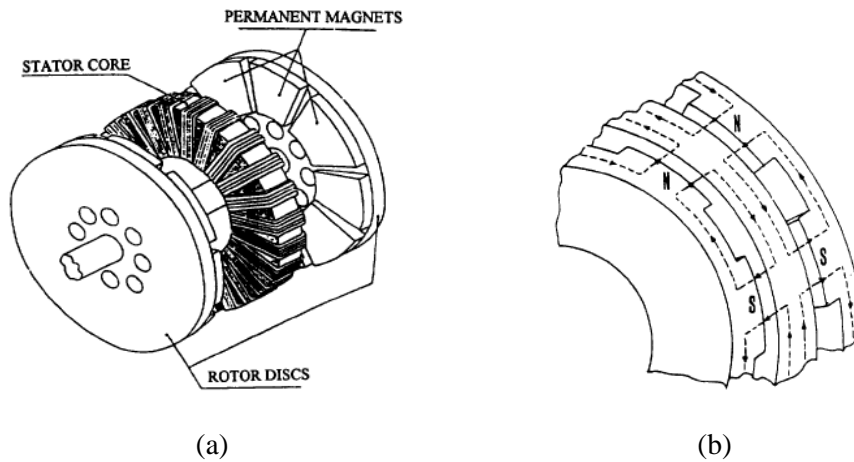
TORUS à bobinage toroïdal : (a) machine éclatée et (b) chemin du flux dans la machine [35].
